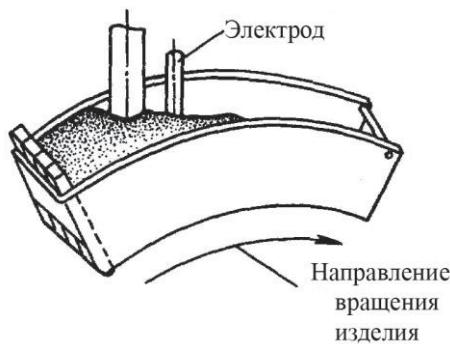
Флюсоудерживающее устройство для сварки кольцевых швов малого диаметра
